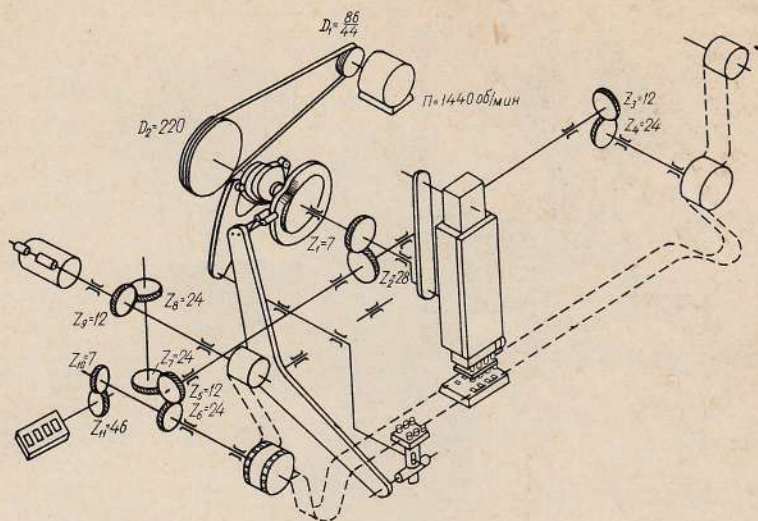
Кинематическая схема станка типа 35-КПП-5
